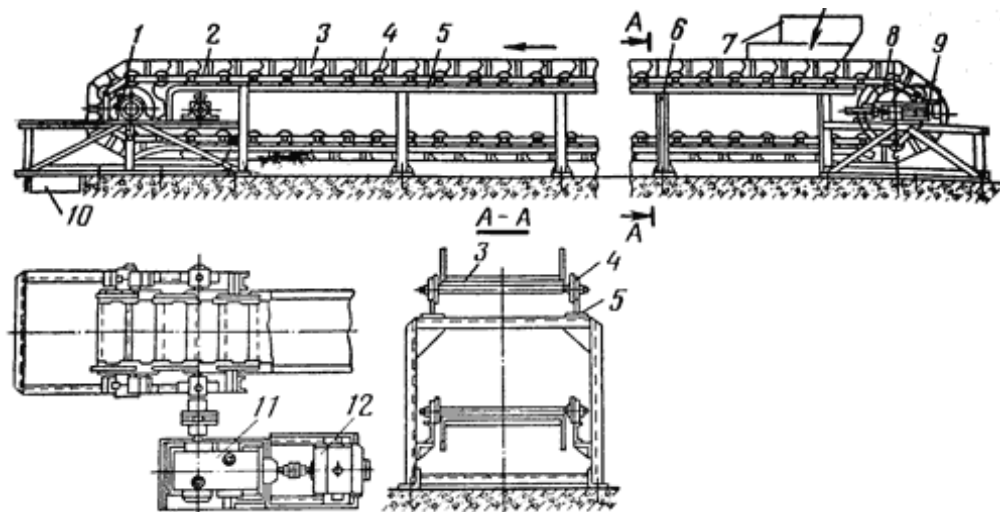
Пластинчастий конвеєр: 1 – привідна зірочка; 2 – ланцюг; 3 – пластина; 4 – каток; 5 – шина напрямної; 6 – станина; 7 – завантажувальна воронка; 8 – натяжна зірочка; 9 – натягач; 10 – розвантажувальна воронка; 11 – редуктор; 12 – електродвигун.
